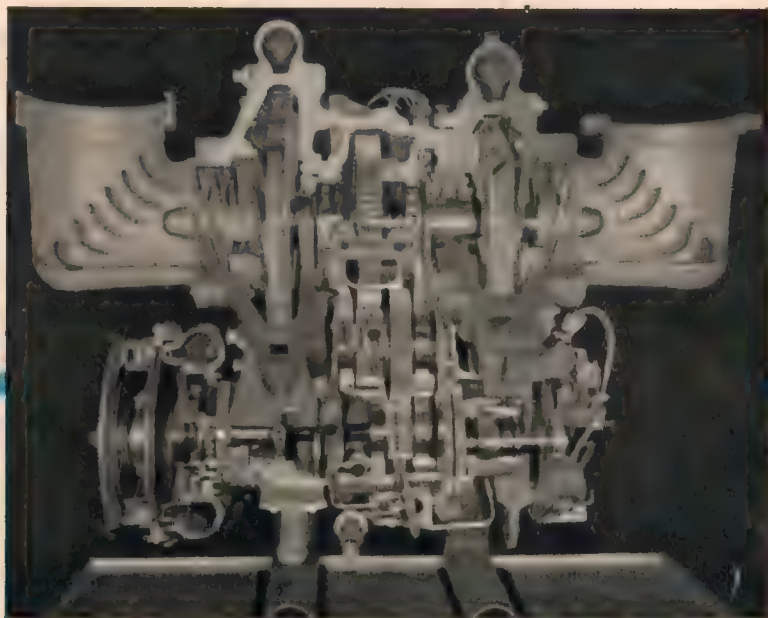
Schnitt durch ein Turbinenpumpenaggregat.
